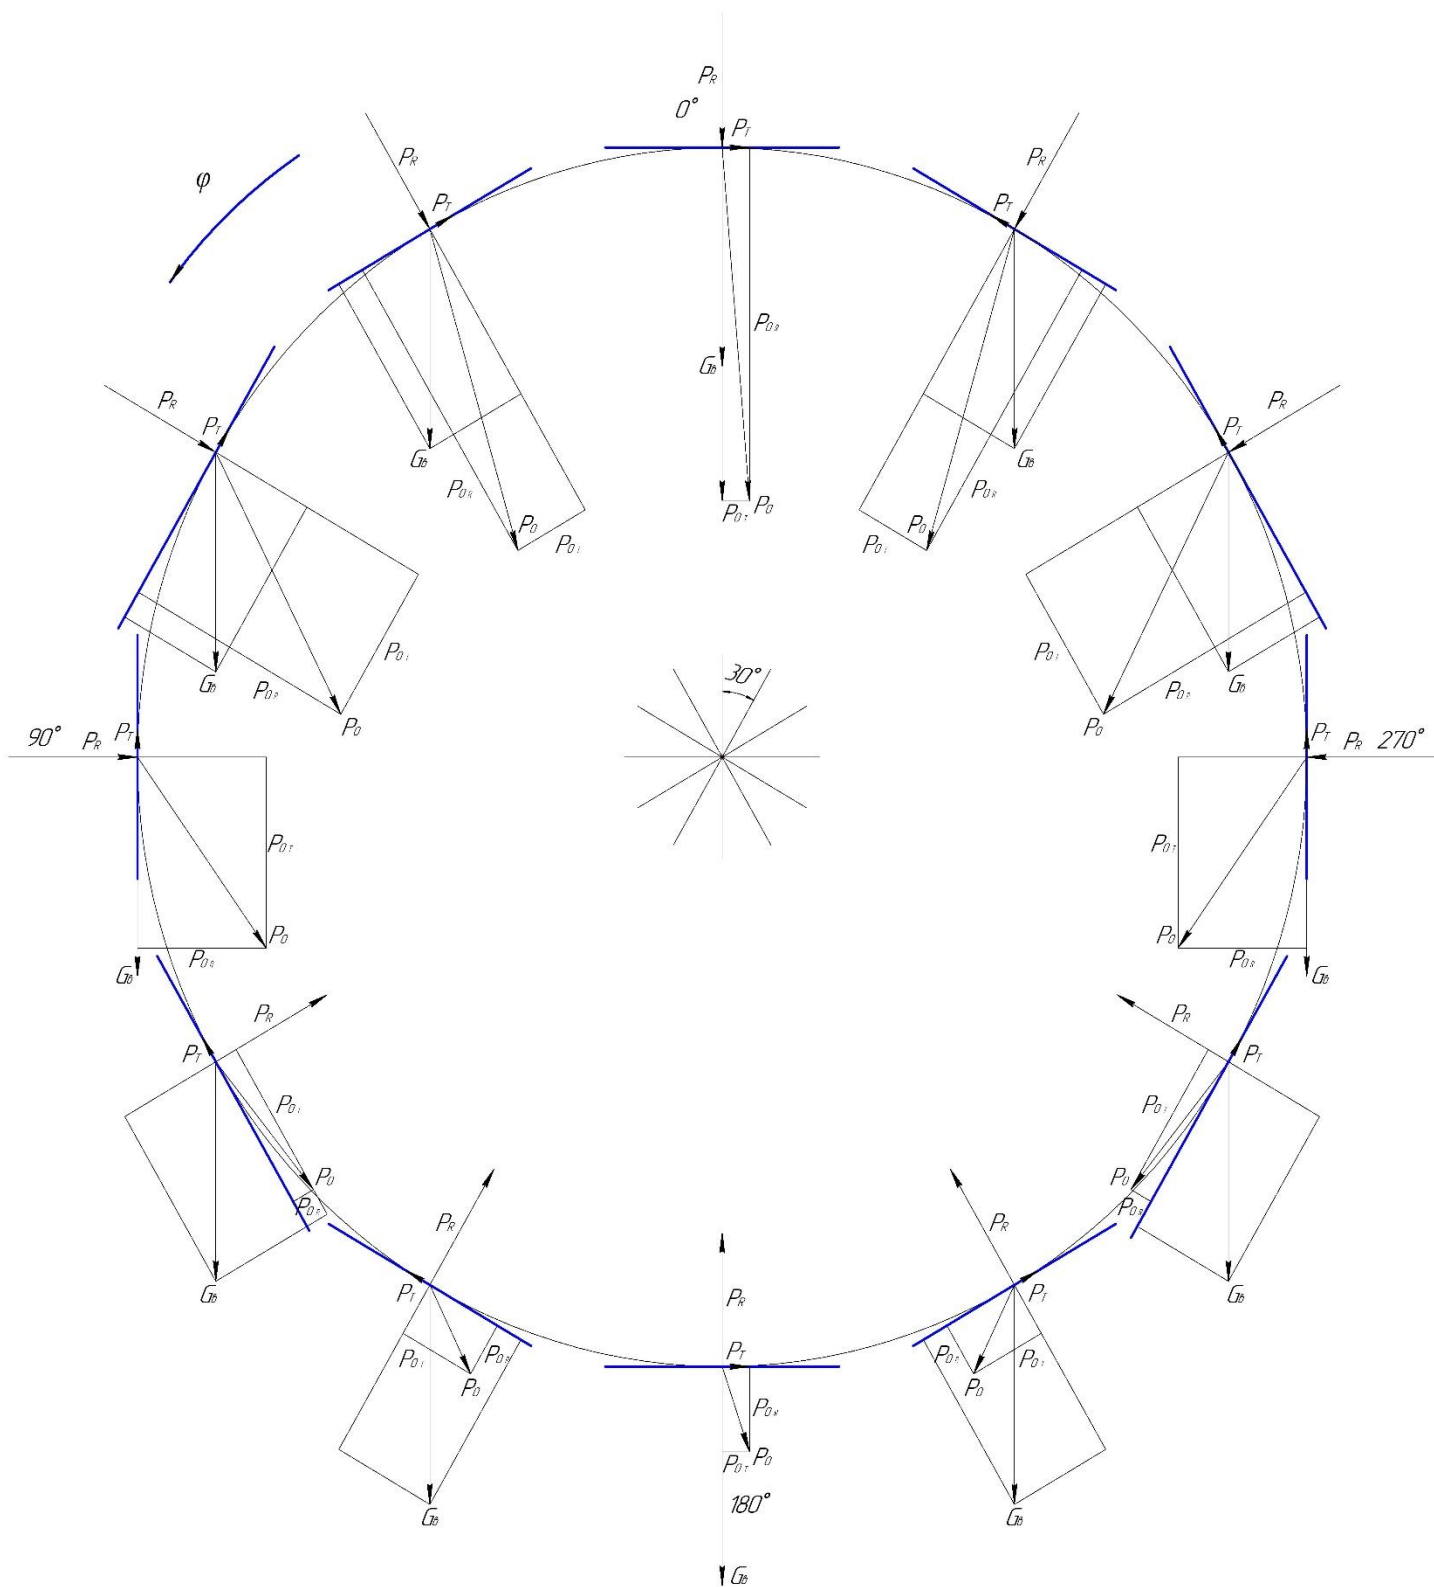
Модель сварочной ванны, показывающая направление равнодействующих сил для каждого положения в масштабе 10:1
